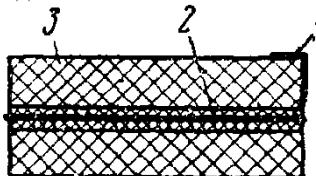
Стержень для электровзрывной запрессовки трубок конденсатора.
